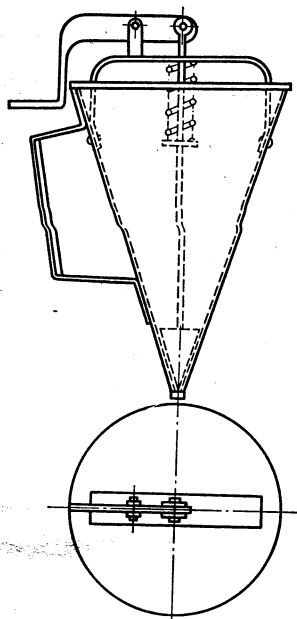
Металлическая воронка с пружинным клапаном для отливки ликерных корпусов конфет
